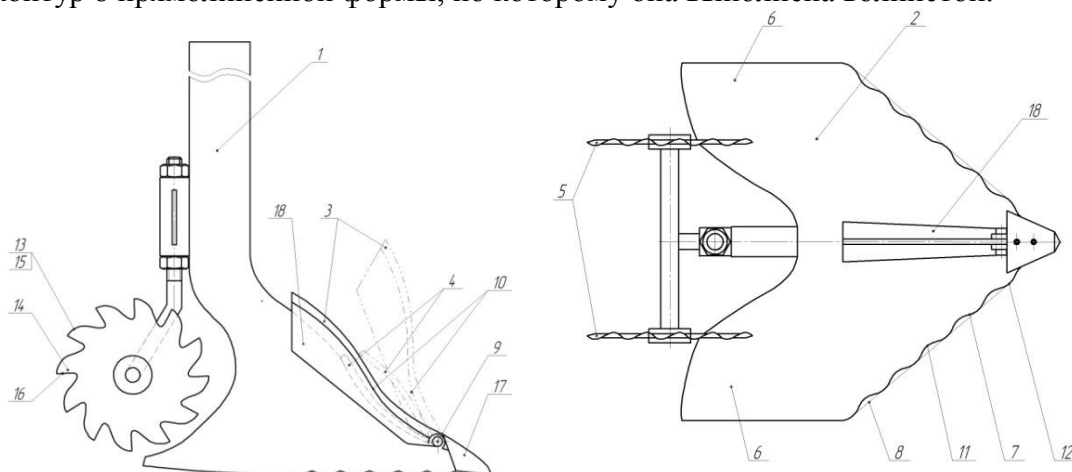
Рабочий орган культиватора: а) вид сбоку; б) вид сверху
